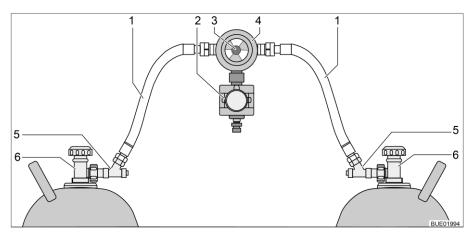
Gasregler mit CPU und Schlauchbruchsicherung
